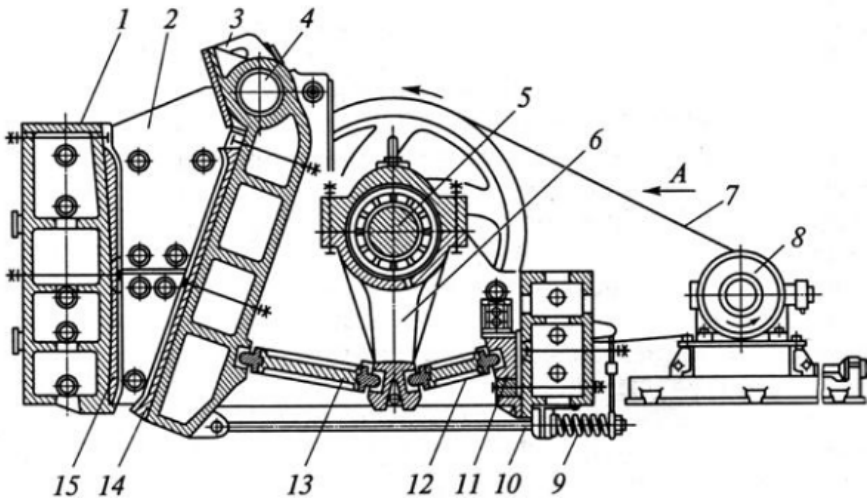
Загальна схема вузла дроблення шокової дробарки
